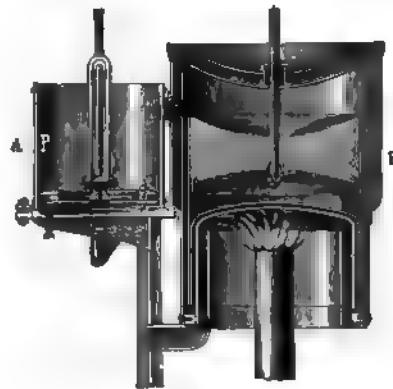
Coupe des cylindres dans la machine Laubereau.
